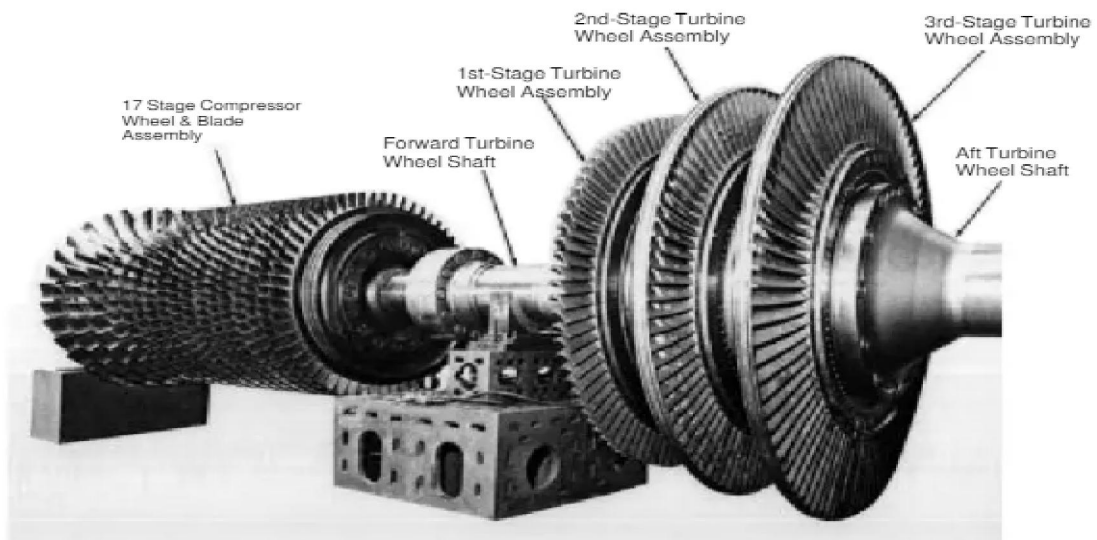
Ensemble de Rotor de compresseur et de Turbine .
